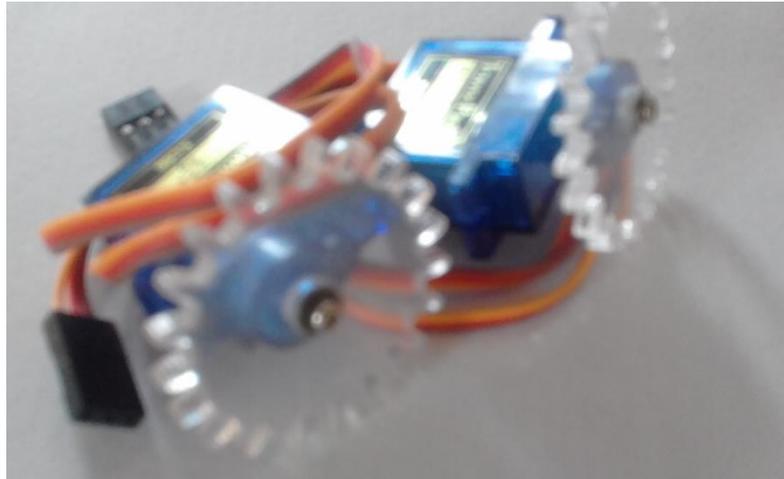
Engranajes posterior al corte en dos materiales diferentes
